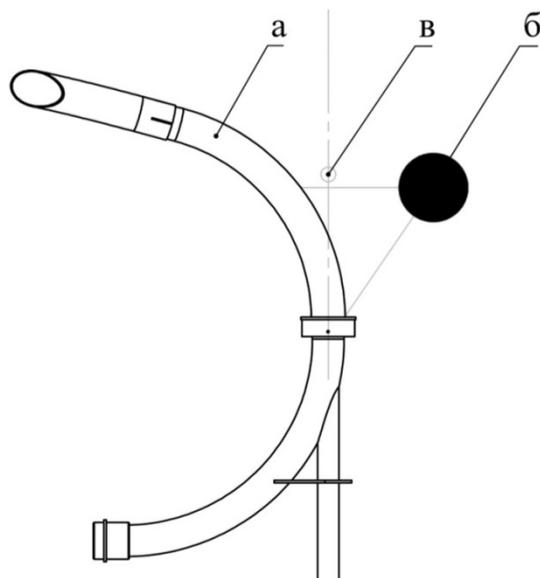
Вращающийся патрубок роторного раздатчика кормов с противовесом:
